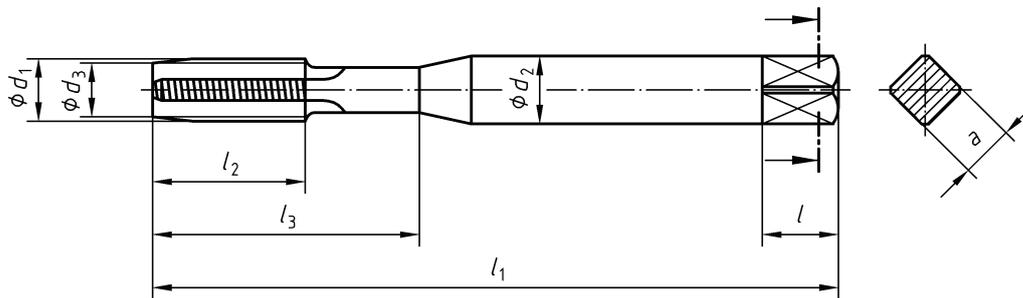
Maschinengewindebohrer EG M2 bis EG M8
